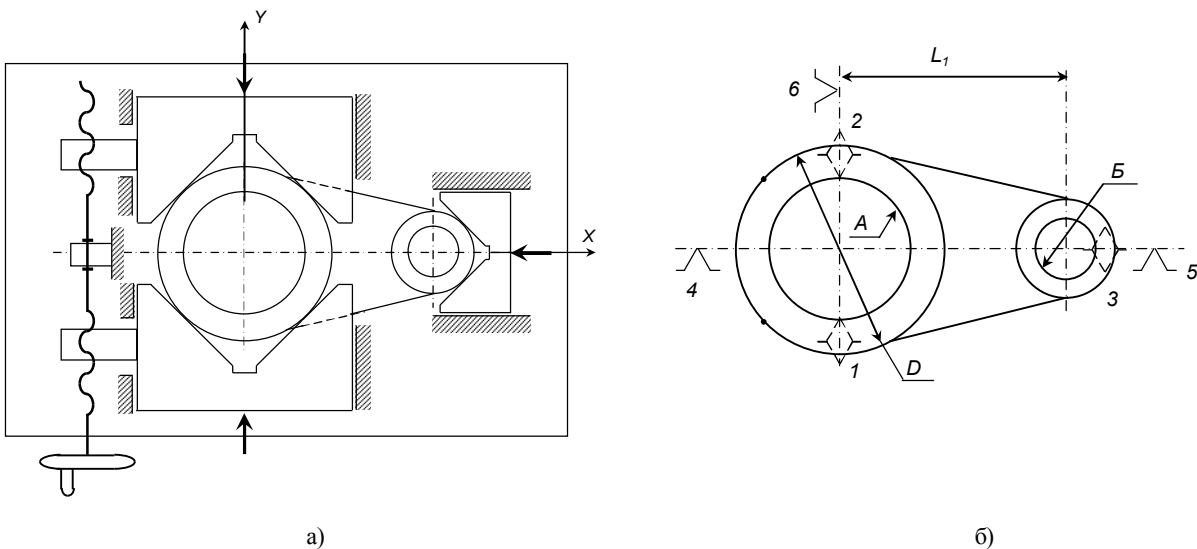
Конструктивна схема верстатного пристрою за варіантом 3 з установленою вихідною заготовкою (а) і схемою базування (б)
